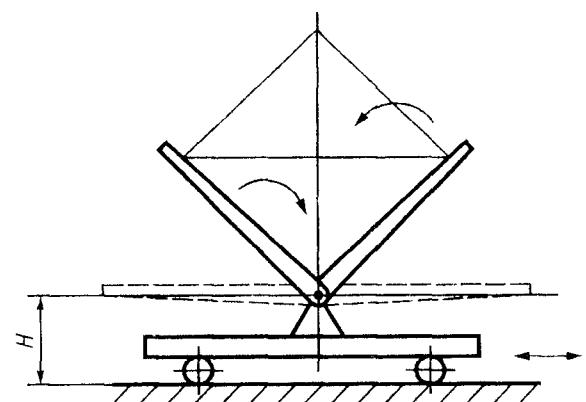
Кантователь рычажный перемещающийся (челночный)
